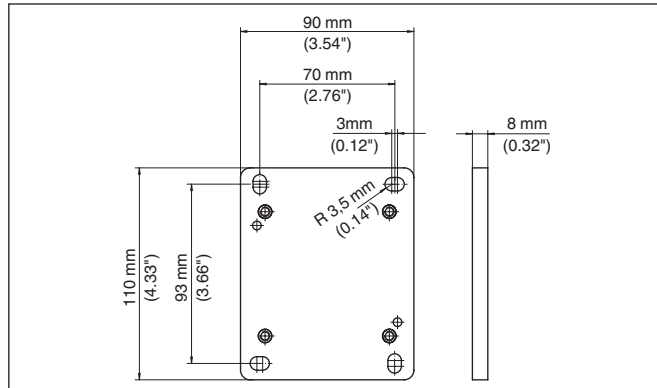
Boorplan - wandmontageplaat (externe behuizing)
